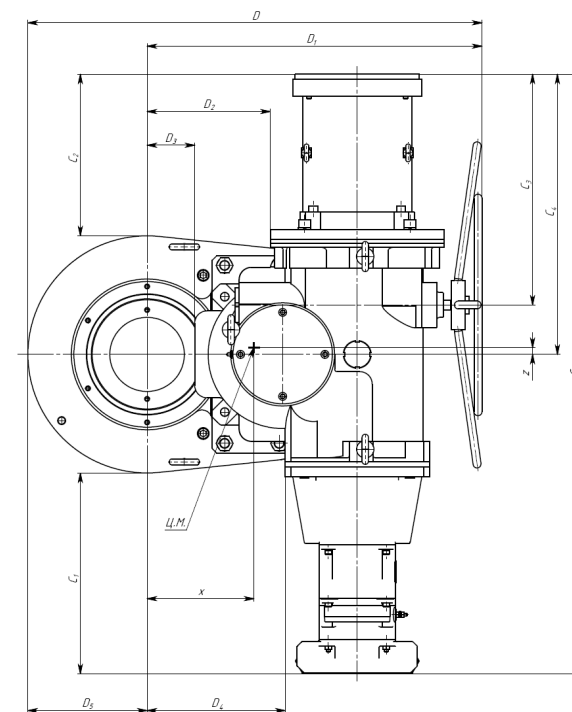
г – Габаритные размеры привода конструктивной схемы 430
